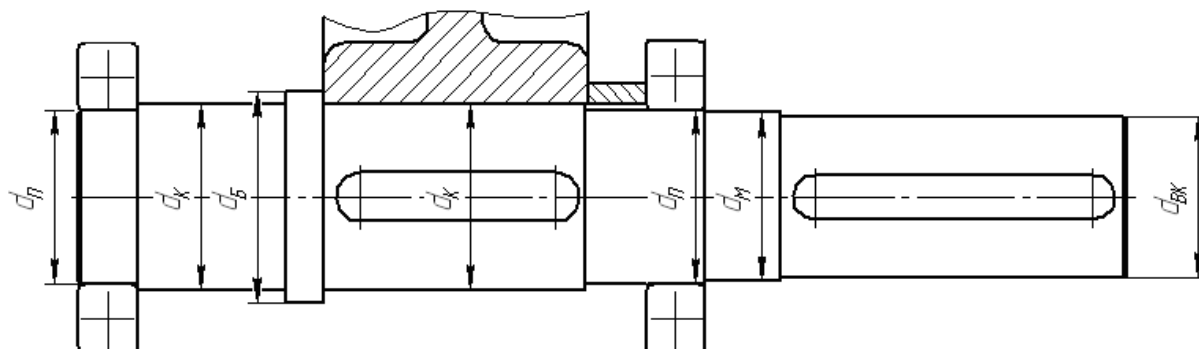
Конструкция тихоходного вала редуктора
